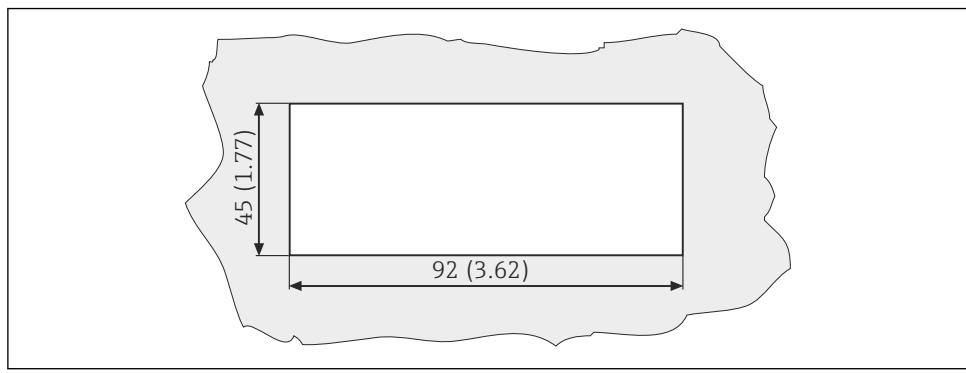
安装孔口的外形尺寸示意图; 单位: mm (in)
